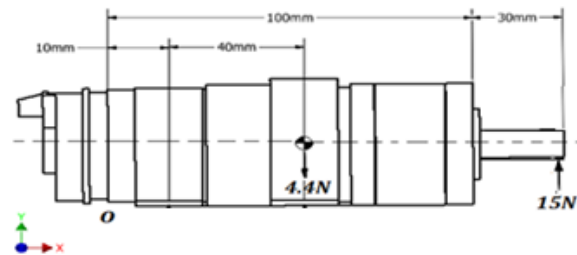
Vista lateral del motor de corte con la ubicación de la fuerza de corte y centro de gravedad.
